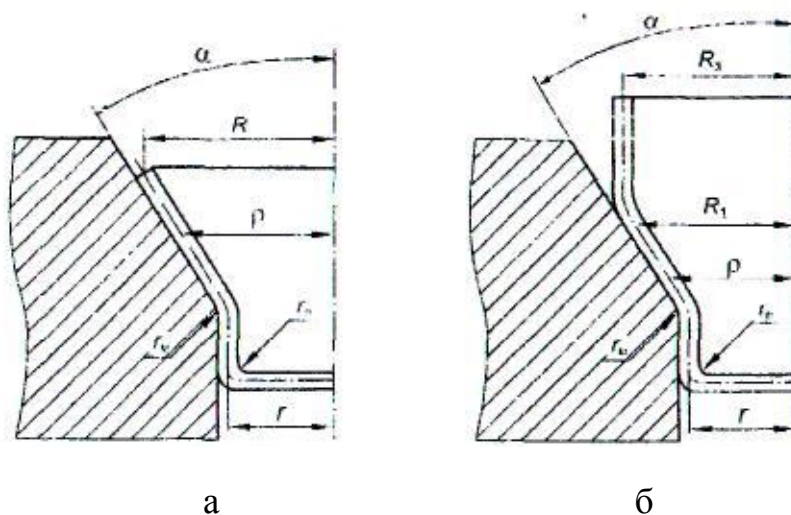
Схема осередку деформації при витяжці циліндричної деталі з плоскої заготовки та наступних переходів витяжки
